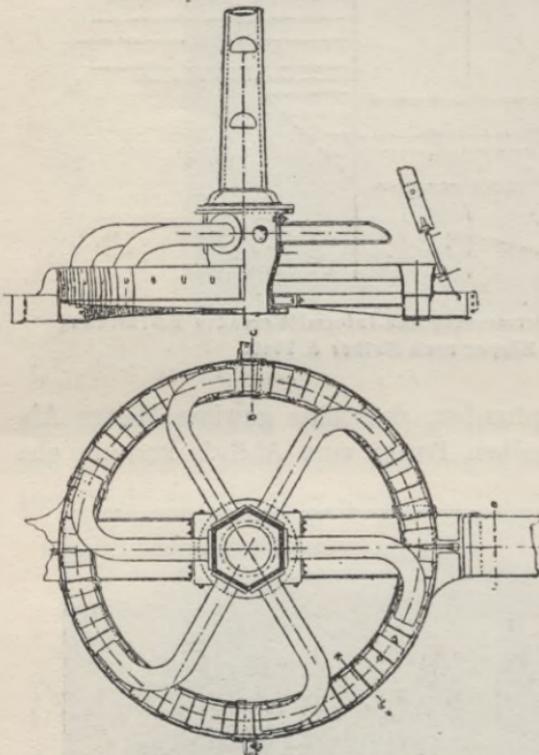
Mather & Platt, Sprenger mit Turbinenantrieb.
